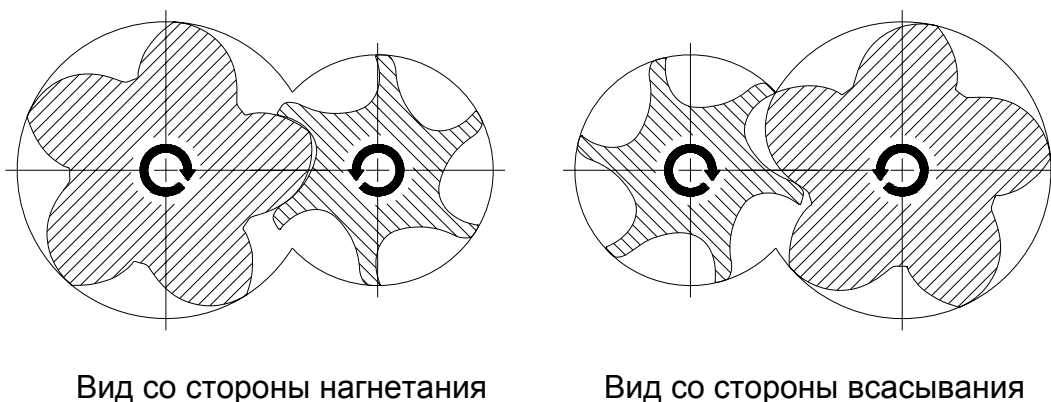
E: внешний вид роторов и правильное направление вращения;
